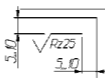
Указание шероховатости, одинаковой для всех поверхностей изделия
